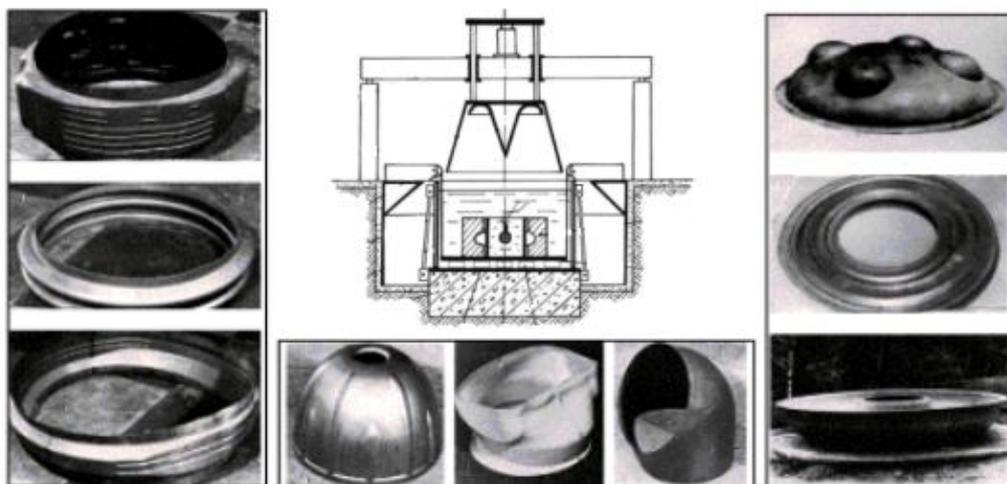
Схема импульсной штамповки и номенклатура изготавливаемых деталей
